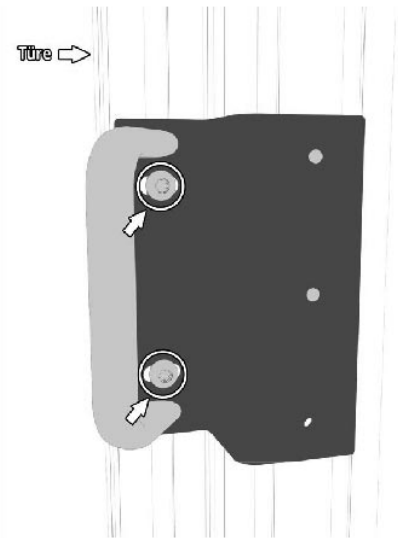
Montageplatte mit Ankerplatte am Profil anbringen und zur Prozesszuhaltung ausrichten. Schrauben M8 x 12 mm Torx festziehen.
